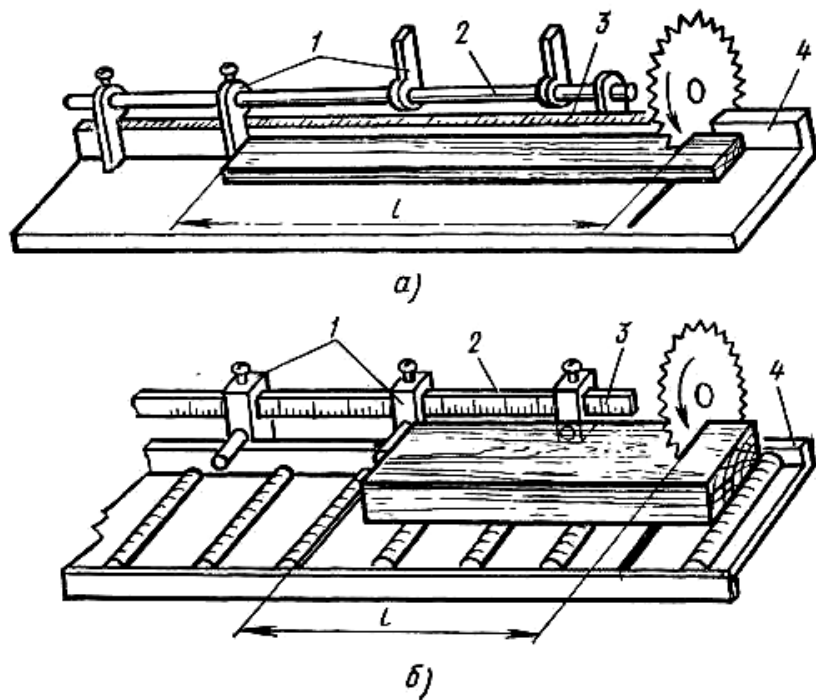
Настройка станка для торцовки деталей по упорам: а — откидным, б — утапливаемым; 1 — упоры, 2 — штанга, 3 — шкала, 4 — направляющая линейка
